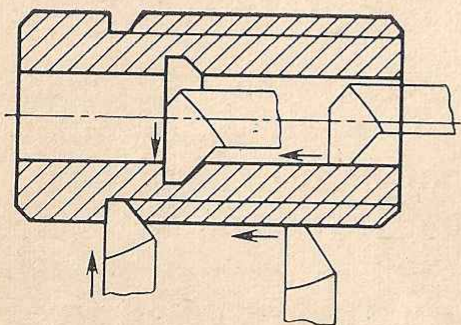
Резцы для нарезания резьбы и проточки канавки
